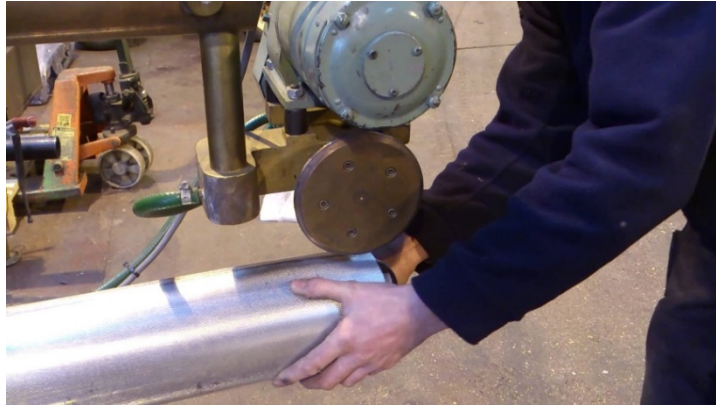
União de conduta em chapa pelo processo de soldadura contínua por resistência [64]
